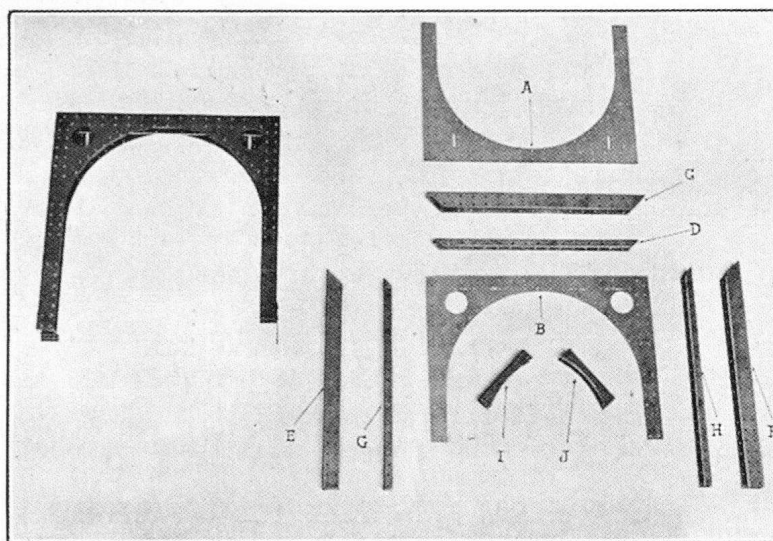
Pièces détachées du Cadre Support de Planiphote
